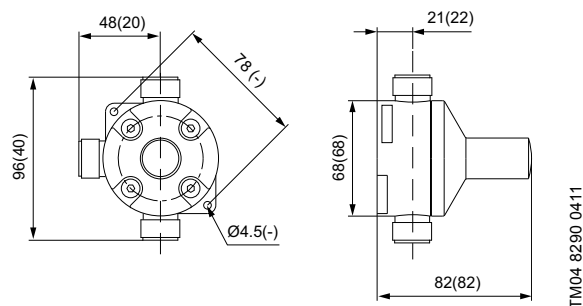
Предохранительный клапан. Размеры, указанные в скобках, относятся к исполнению из нержавеющей стали.
